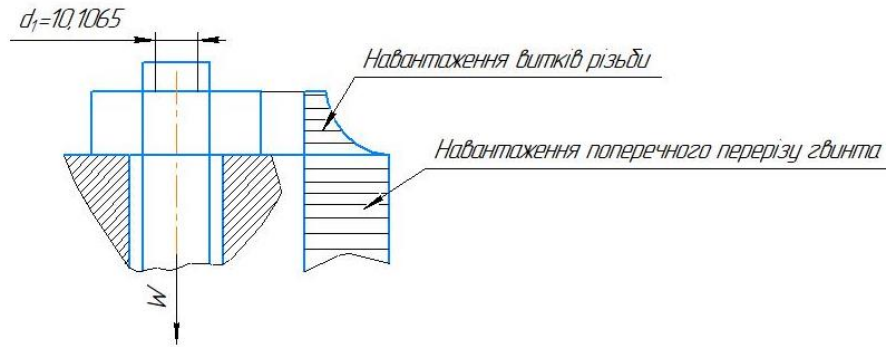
Розрахункова схема навантаження різьбового ділянки штока
